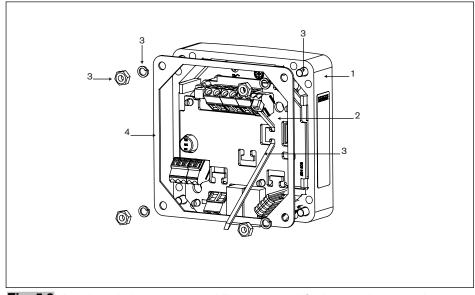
Despiece de los repuestos del Tipo 8025, versión de montaje en panel
